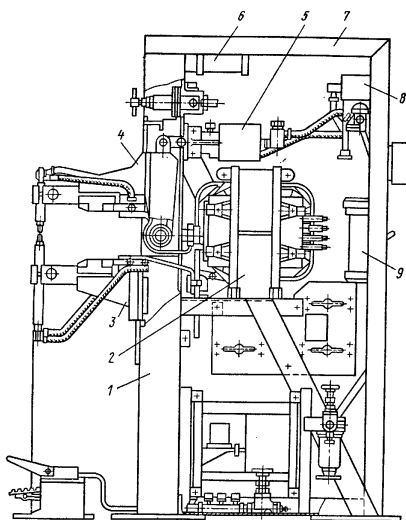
Машина типа МТ-810 для точечной сварки:
